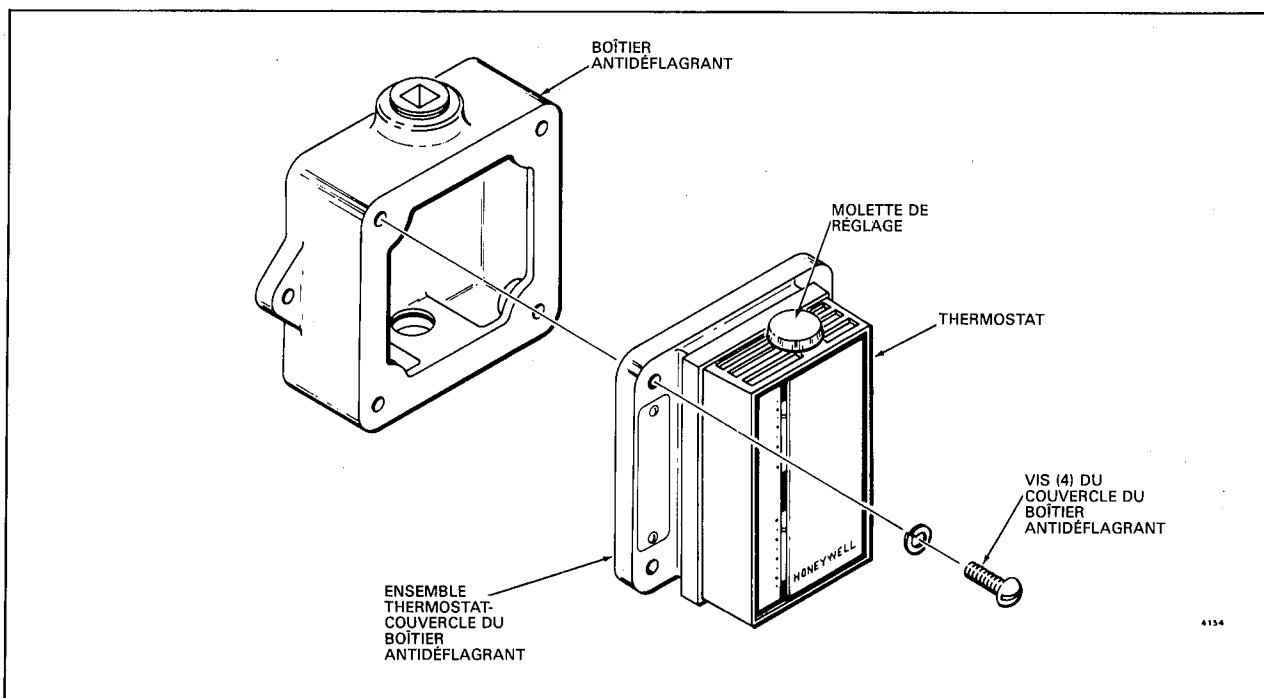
MONTAGE DU THERMOSTAT T6051B.
